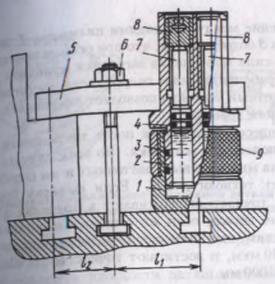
Скема установки универсального силового гидроцилиндра на станке
